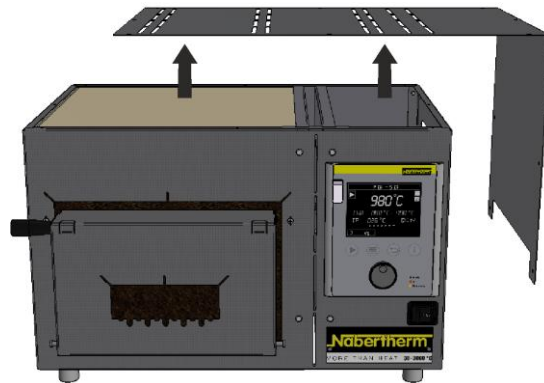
Lösen der Gehäuseschrauben und Entfernen des Deckels
